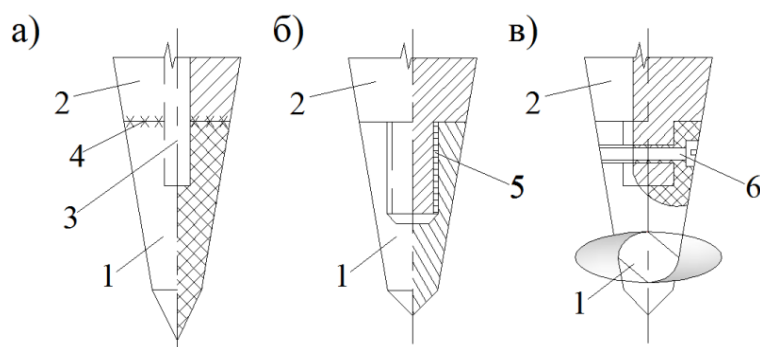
Типовые схемы наконечников РСу упрощенной (а), инвентарной (б) и сложной (в) конструкции: 1- наконечник; 2- коническая часть РСу; 3- вал РСу; 4- сварное соединение; 5- резьбовое соединение; 6- болтовое соединение.
